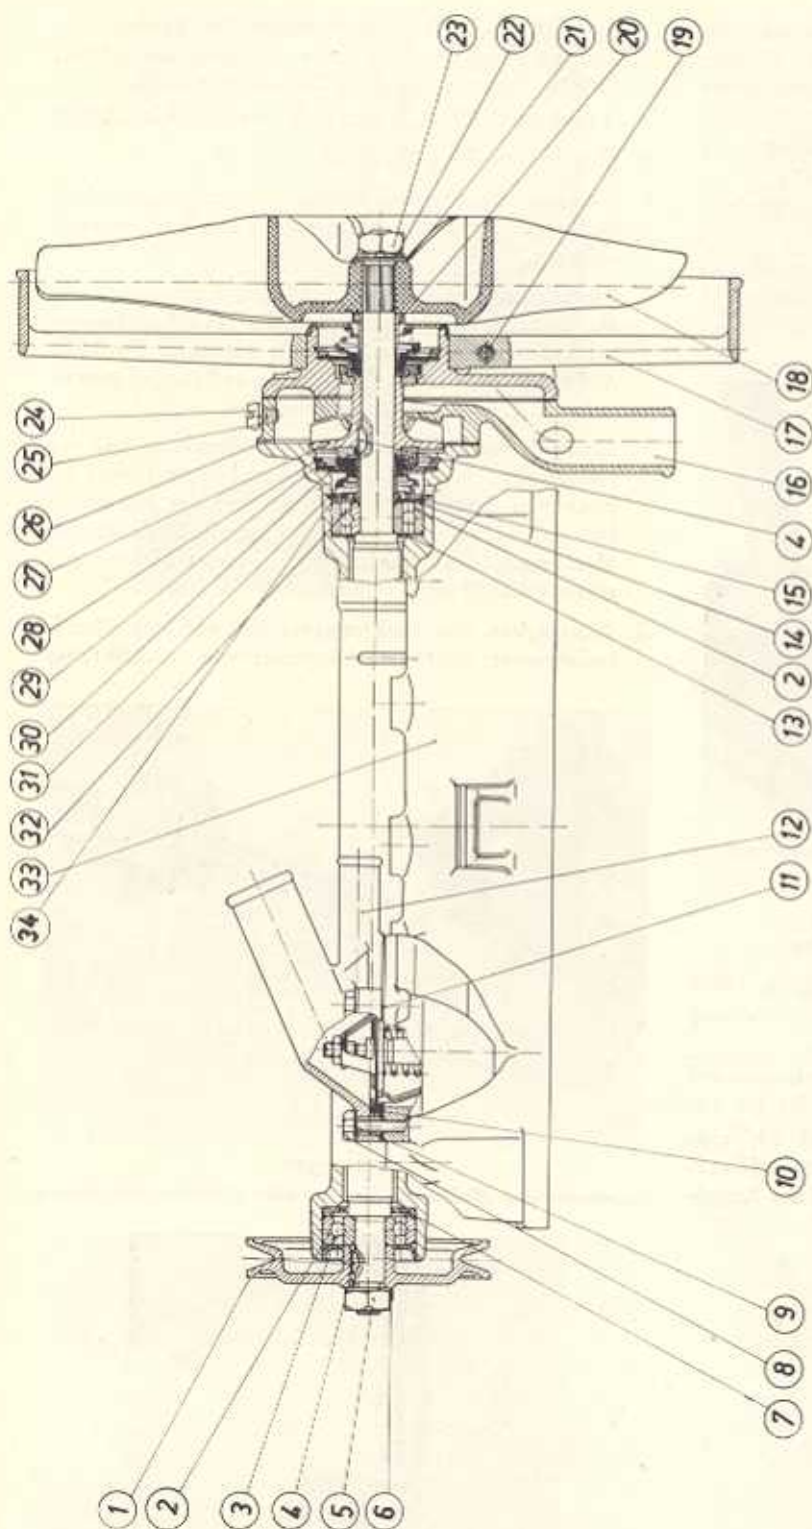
Zylinderkopf mit Einbauwasserpumpe (Schnittzeichnung)
